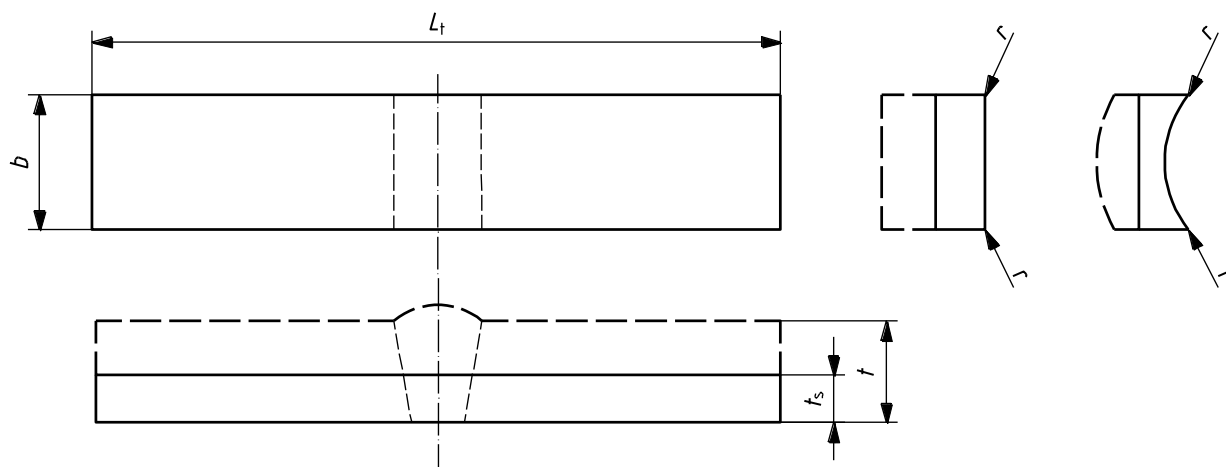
Поперечный образец для испытаний стыковых сварных швов на загиб с растяжением корневой стороны (TRBB)
